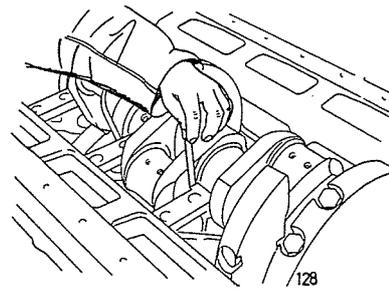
Kontrolle des Achsalspiels der Kurbelwelle mittels Fühlerlehre
